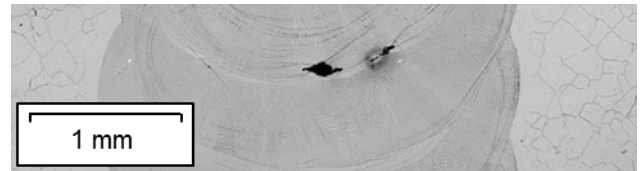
Makroschliffe der Schweißverbindungen
